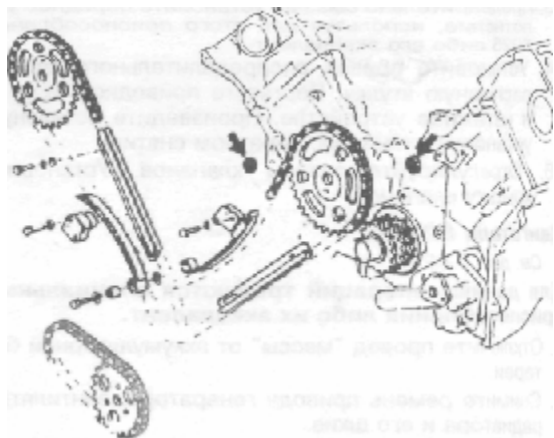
Натяжное устройство цепи и цепь Двигатель В280F
